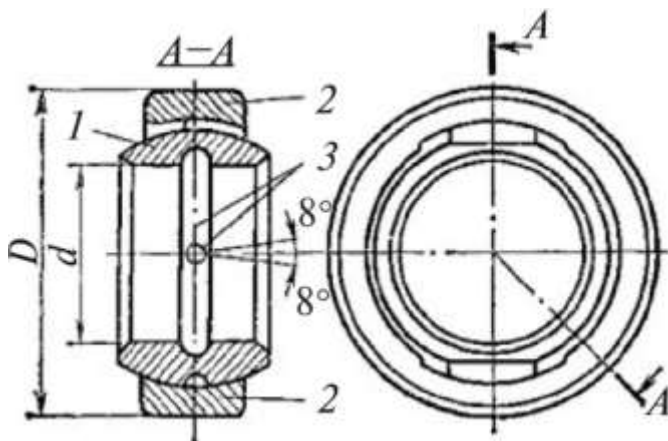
Подшипники с самоустанавливающимися вкладышами
